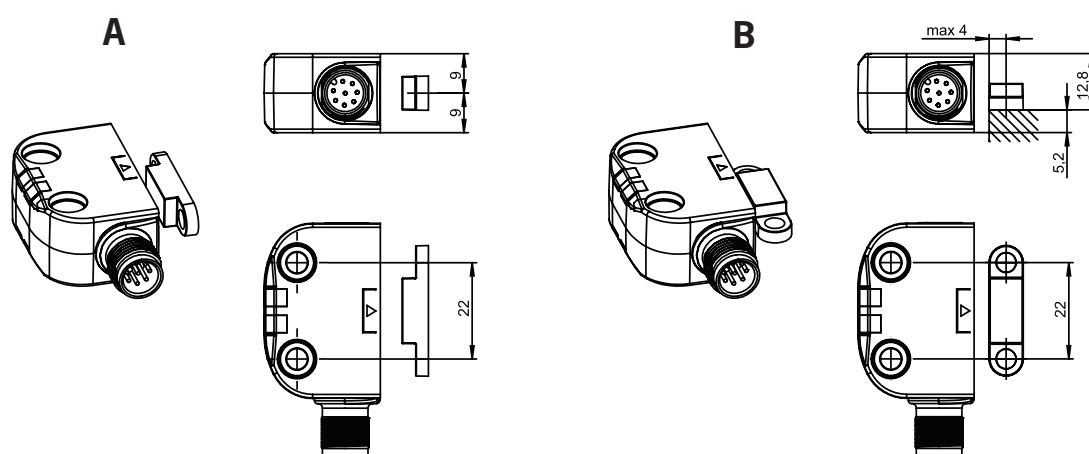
Posiciones de montaje admitidas para el actuador A-C11-01-...
